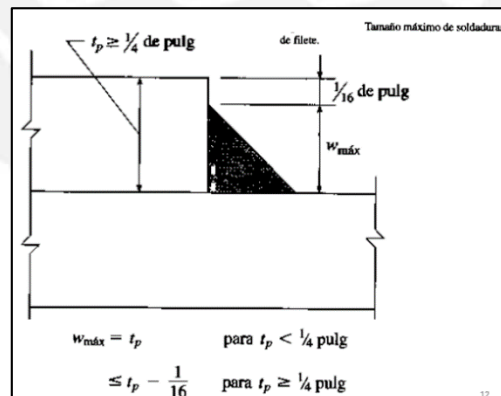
TAMAÑOS MÁXIMOS DE CATETO DE SOLDADURA FILETE SEGÚN ESPESOR DE MATERIAL (FUENTE: NORMA AMERICANA AWS)
